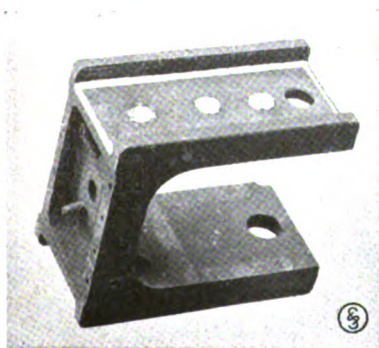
Durch Lichtbogenschweißung instand gesetztes Achslager.
